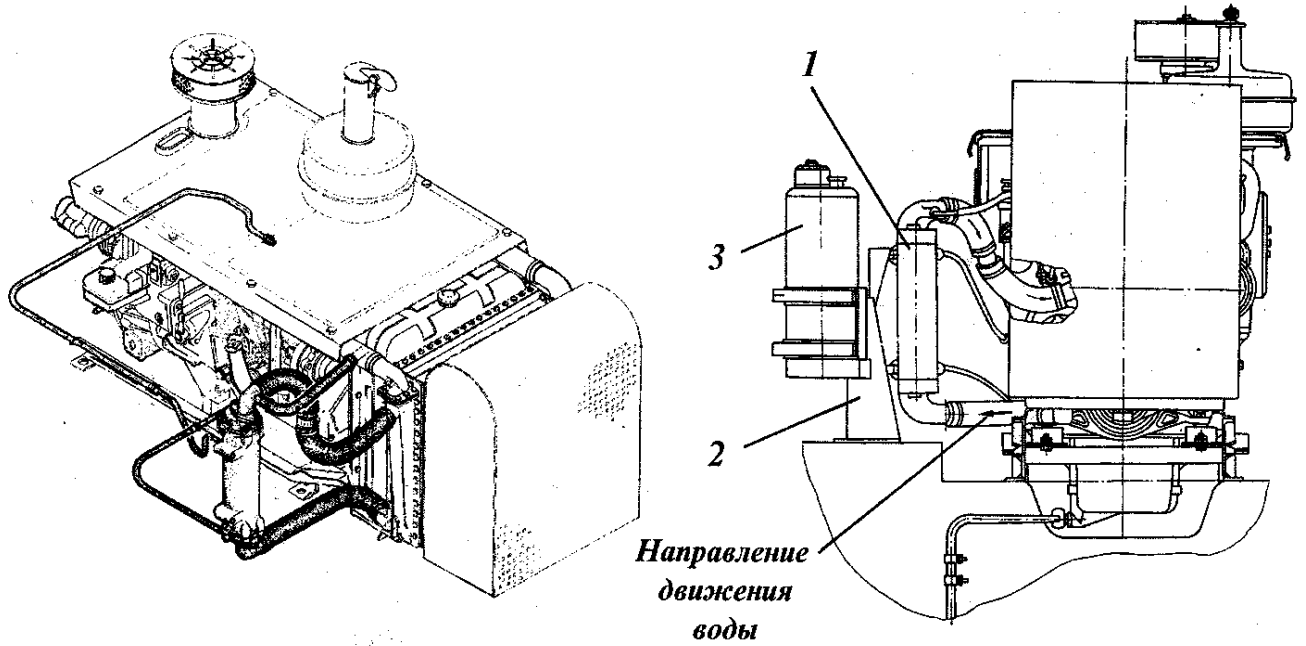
Моторная установка с двигателем Д442-53Р/55Р
